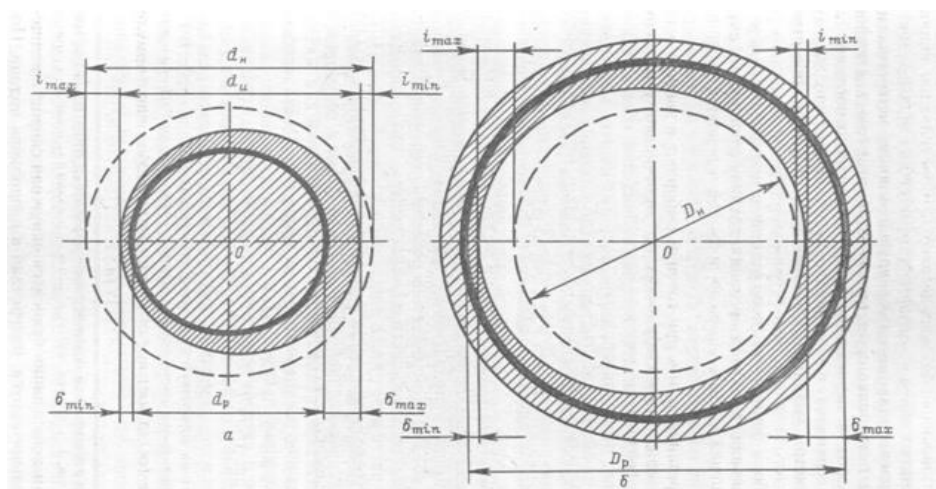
Схемы обработки вала и отверстия под ремонтный размер.
